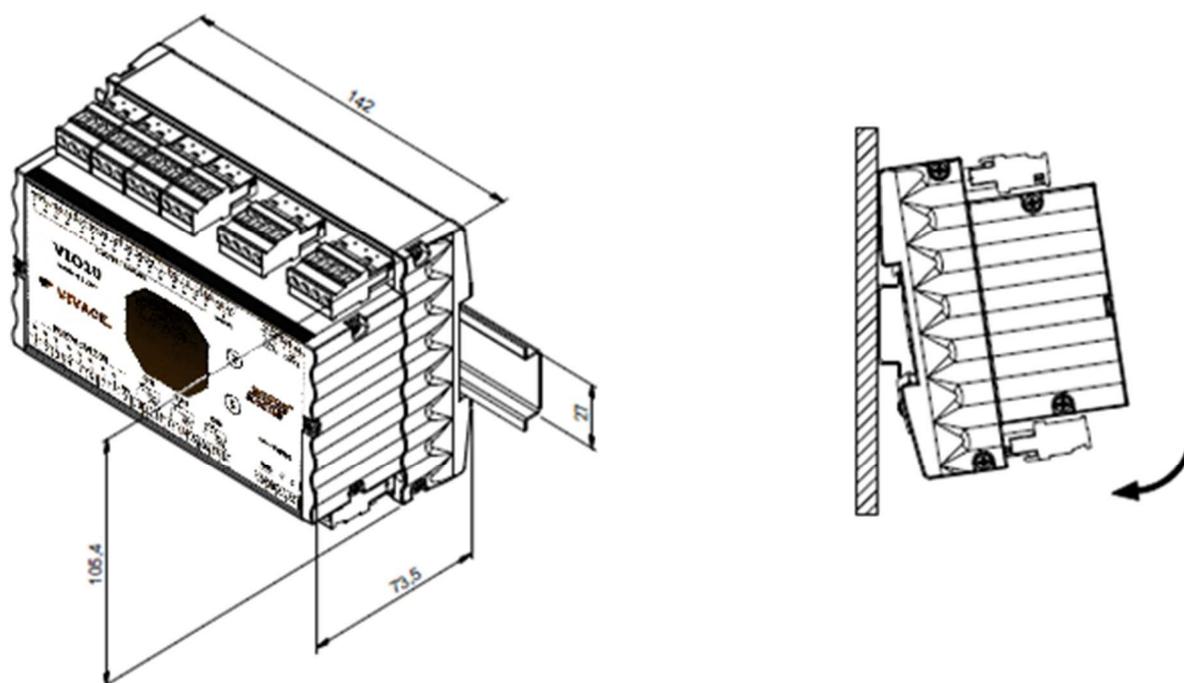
Dibujo dimensional y esquema de montaje de la VIO10-P.
